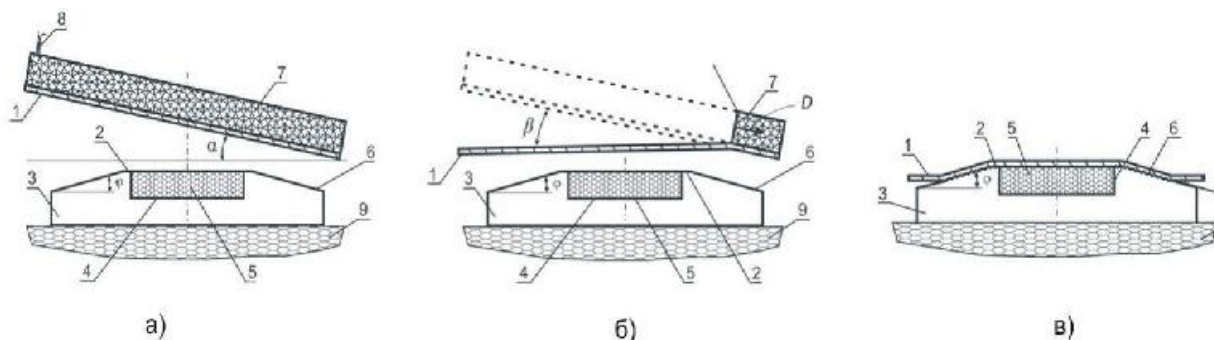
Комбинированная схема компактирования и сварки взрывом
